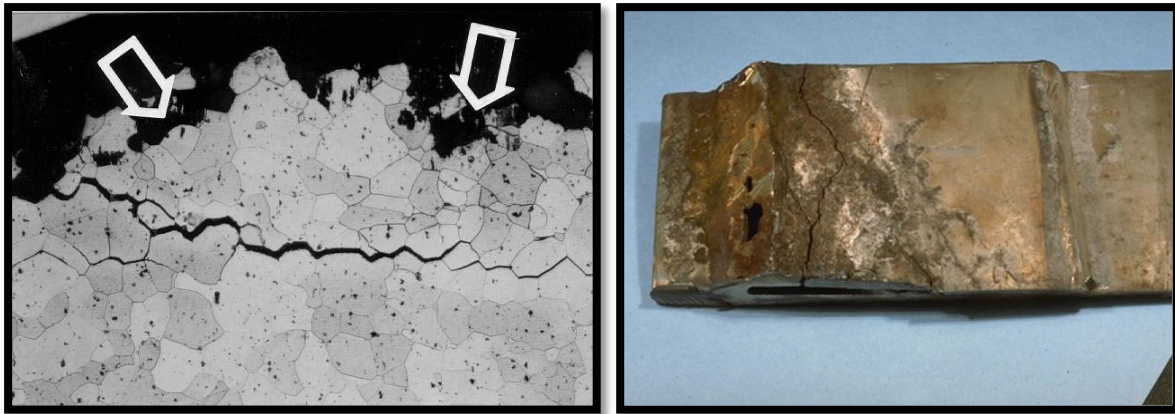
Corrosion sous contrainte : Corrosion sous tension dans une structure soudée d'acier allié (efforts induits par la soudure).
